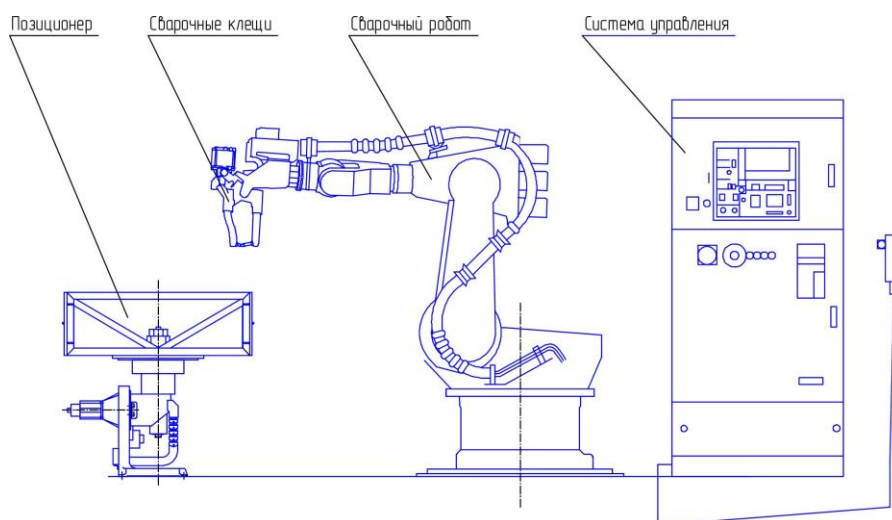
Использование сварочного робота с закрепленными на конце манипулятора сварочными клещами
